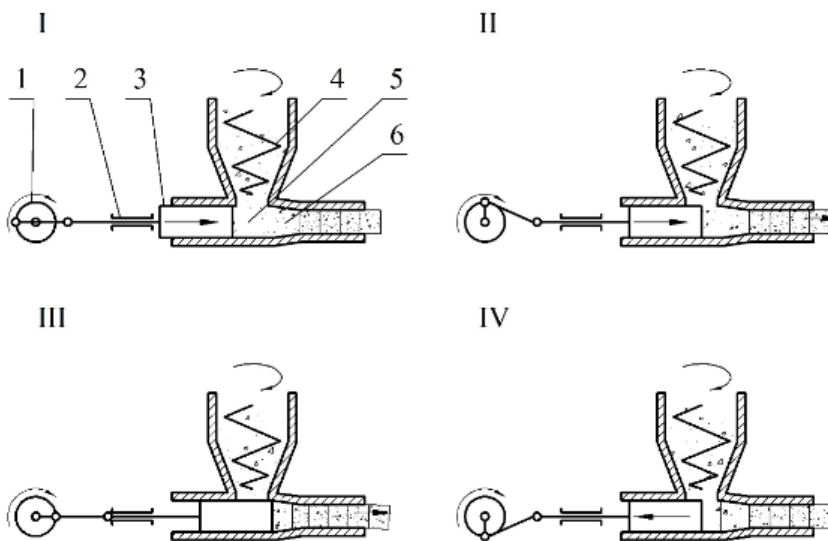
Схема роботи поршневого пресу: 1 – шатунний або ексцентричний механізм, 2 – повзунок, 3 – штампувальний поршень, 4 – механізм подачі сировини, 5 – ущільнювальна камера, 6 – пресувальна камера [5]
